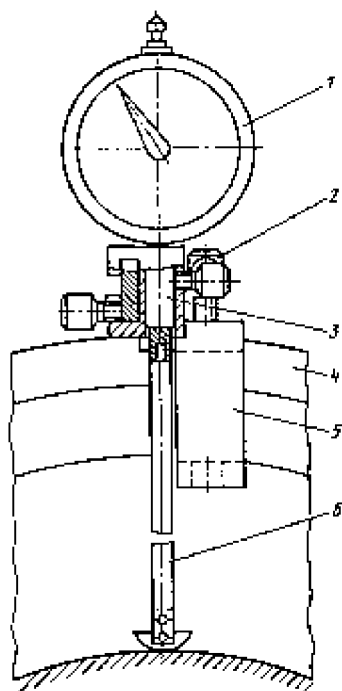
Пристрій ПКВД-М контролю параметрів колектора тягового електродвигуна: 1 – індикатор годинникового типу; 2 – фіксуючий пристрій; 3 – направляюча; 4 – статор ТЕД; 5 – корпус; 6 – штанга
